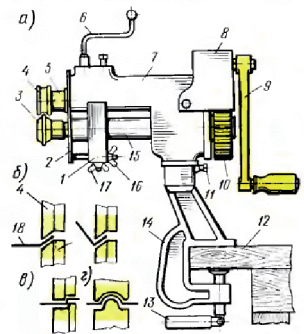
Прокатка валиков жесткости на ручной настольной зиг-машине: *a* — зиг-машина, *б* — прокатка бортика под углом 90° , *в* — прокатка двойного бортика, *г* — выкатка валика жесткости; 1 — скользящий, 2 — ограничительная рамка, 3, 4 — нижний и верхний ролики, 5, 13 — верхний и нижний валки, 6 — рычажный винт, 7 — корпус, 8 — кожух, 9 — рукоятка, 10 — зубчатый механизм, 11 — винт для изменения положения корпуса на кронштейне, 12 — верстак, 13 — зажимной винт, 14 — кронштейн, 16 — винт ограничительной рамки, 17 — винт для закрепления скользящего, 18 — обрабатываемая деталь
